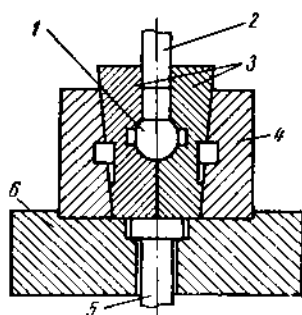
Схема устройства закрытого штампа для штамповки поковки головки рычага на фрикционном прессе
